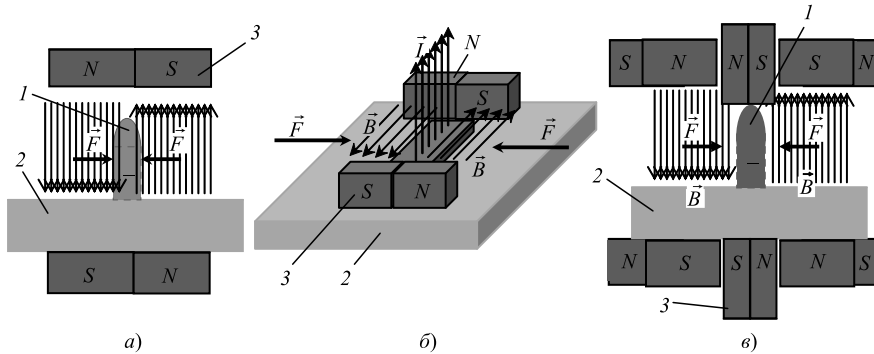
Схемы приложения боковой сжимающей силы к сварочной ванне с обеих сторон:
